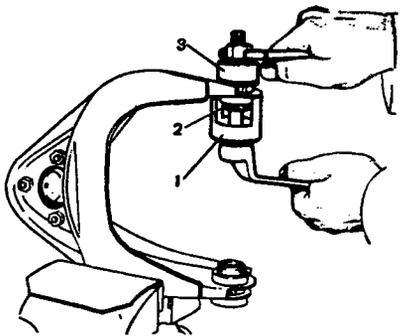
Запрессовка шарниров верхнего рычага: 1 - приспособление А.47046; 2 - шарнир; 3 - колпачок, применяемый вместе с приспособлением А.47046
